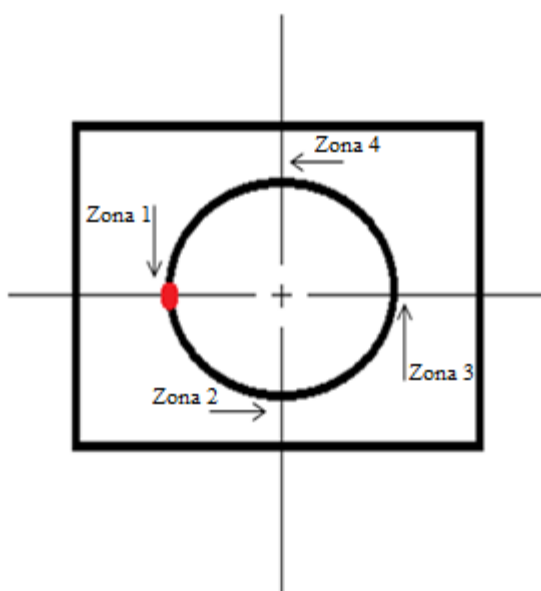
Zonas de corte: a zona 1 corresponde ao início de soldadura. Vista de topo do tubo de menor diâmetro
